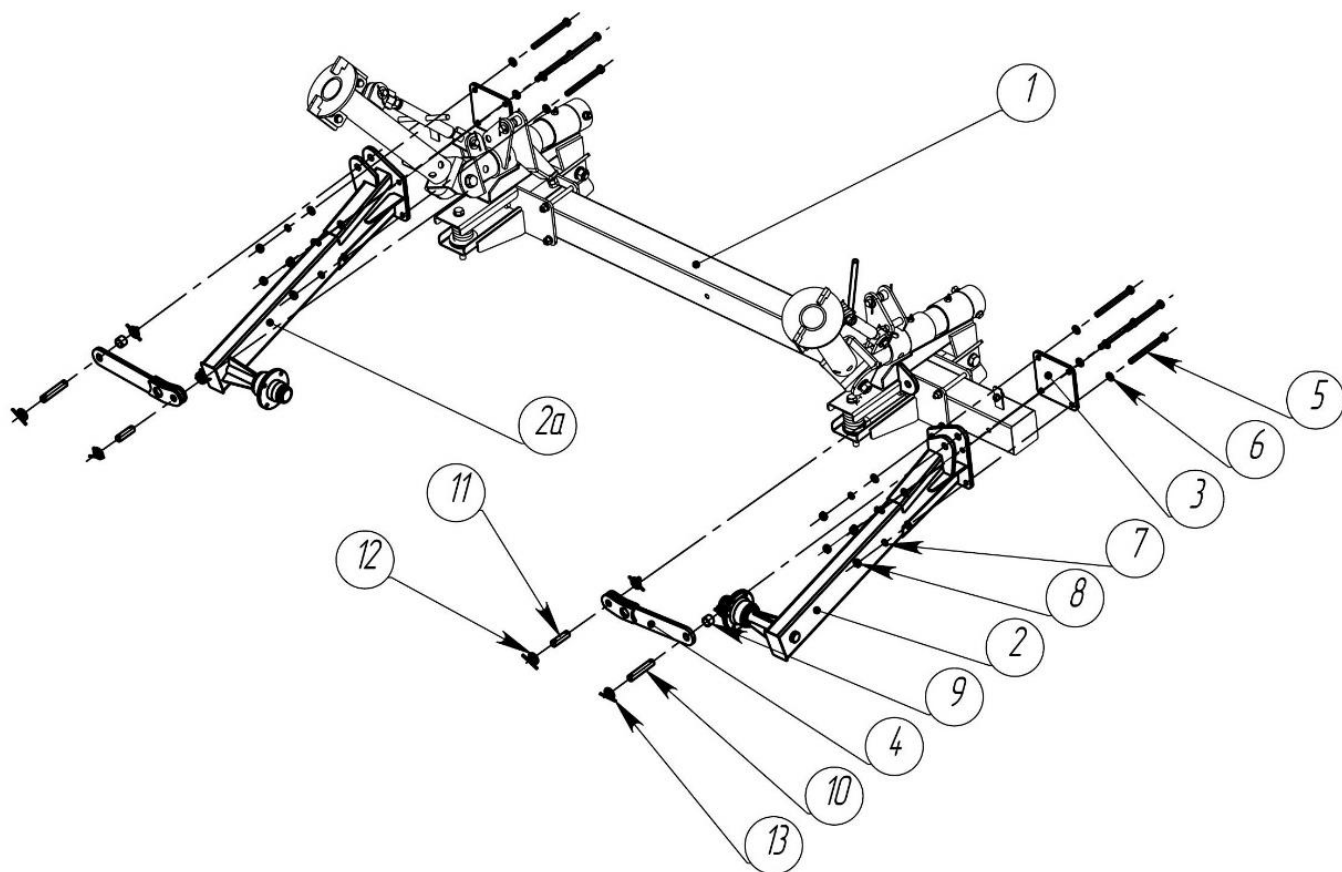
Установка опорной балки колеса (Общий вид)
